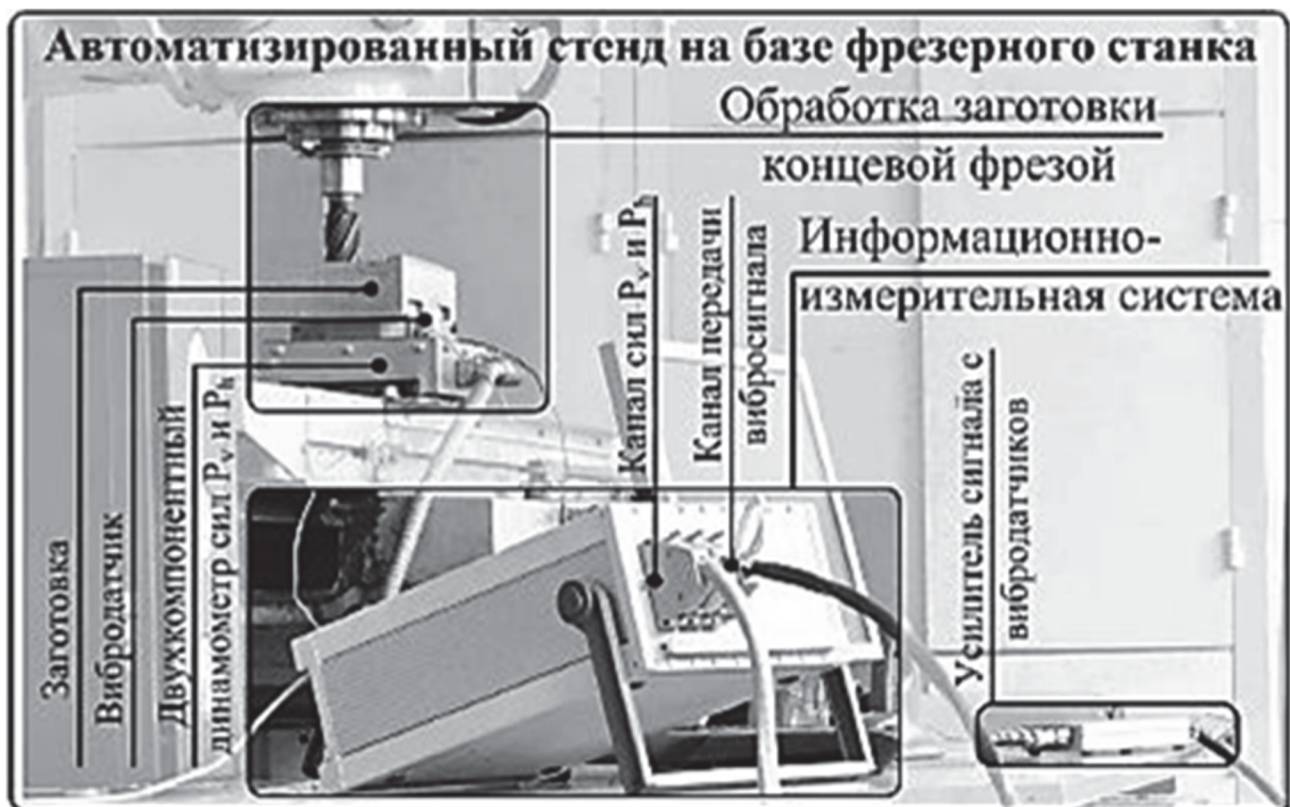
Схема автоматизированного стенда, построенного на базе фрезерного трехкоординатного станка с ЧПУ
